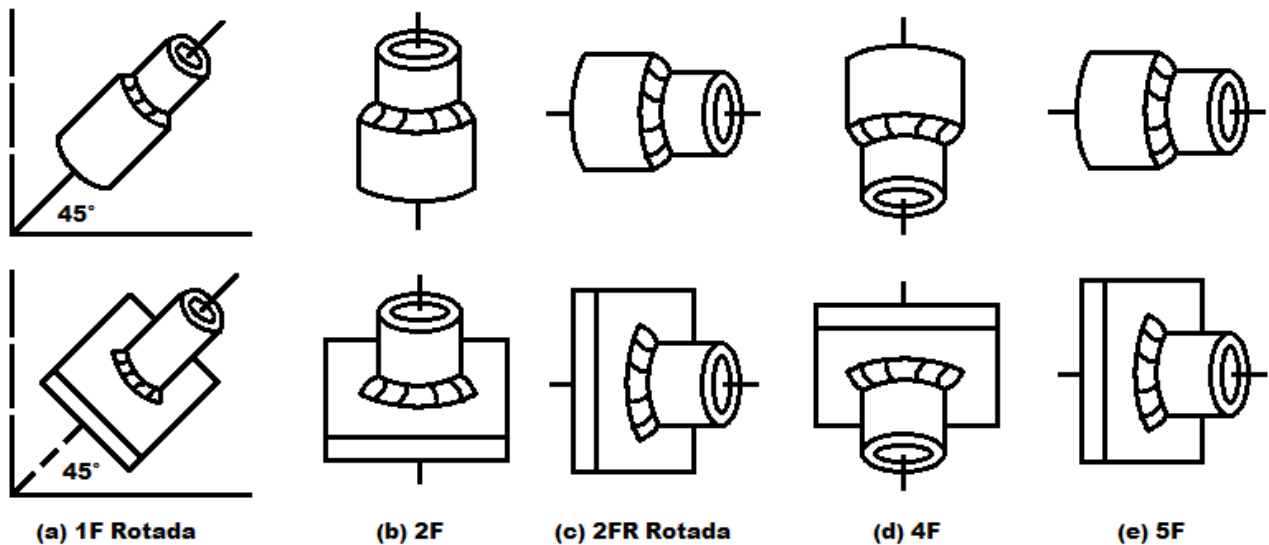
Posiciones de calificación de soldadores en filete sobre platina y tubería, según código ASME BPVC Sección IX (2, 111)
